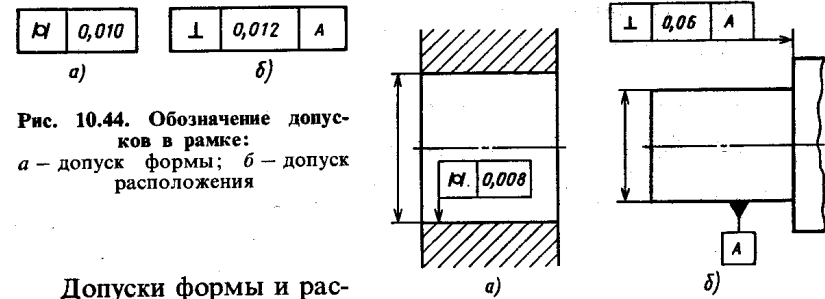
Обозначение допусков в рамке: а — допуск формы; б — допуск расположения
